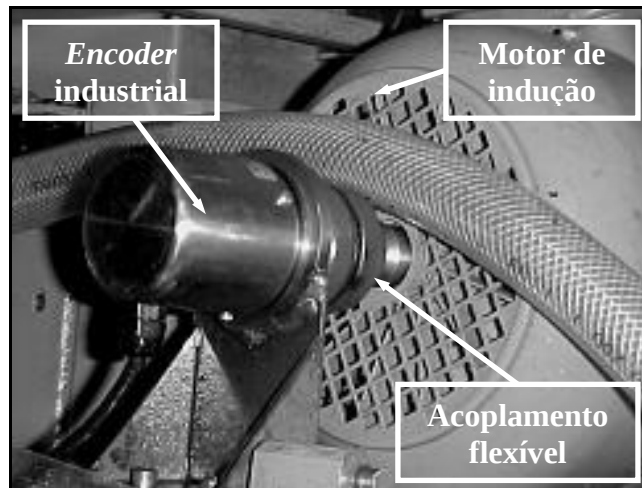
Fixação do *encoder* no eixo do motor do cabeçote porta-rebolo.
